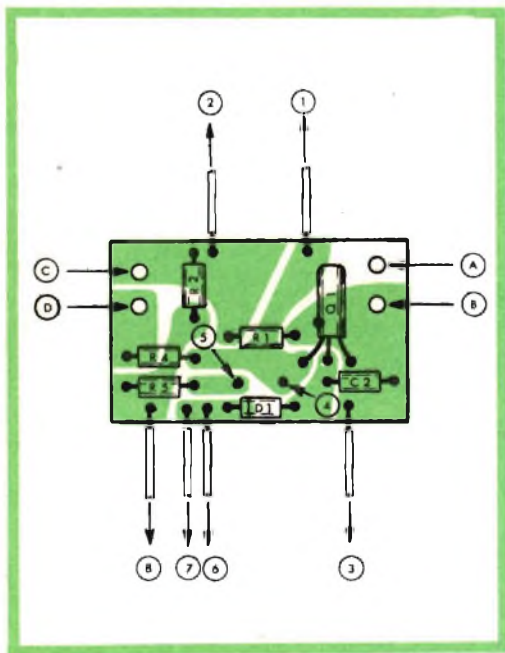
Disposizione delle parti sulla plastrina di bachelite recante il circuito stampato.
